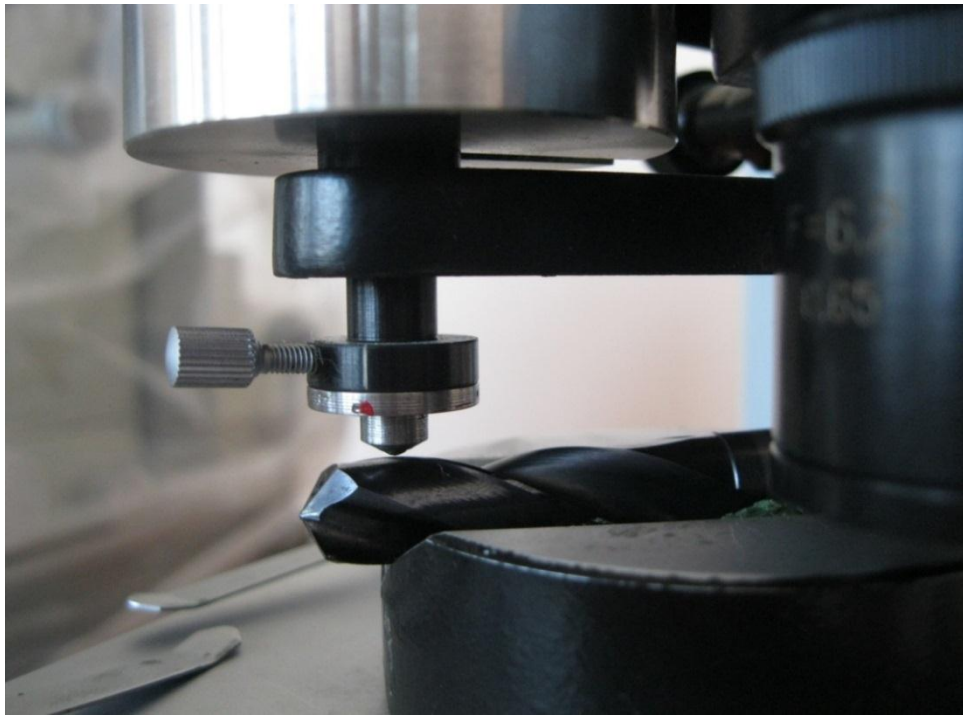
вимірювання поверхневої твердості свердел із швидкорізальної сталі
